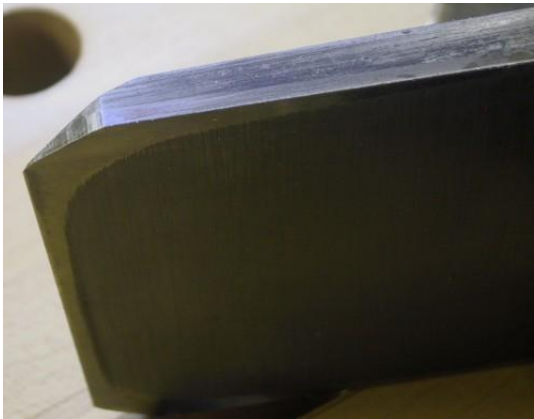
Fer japonais. L'acier extrêmement dur de la planche est soudé par forge à l'acier extra doux de la masse du fer.
